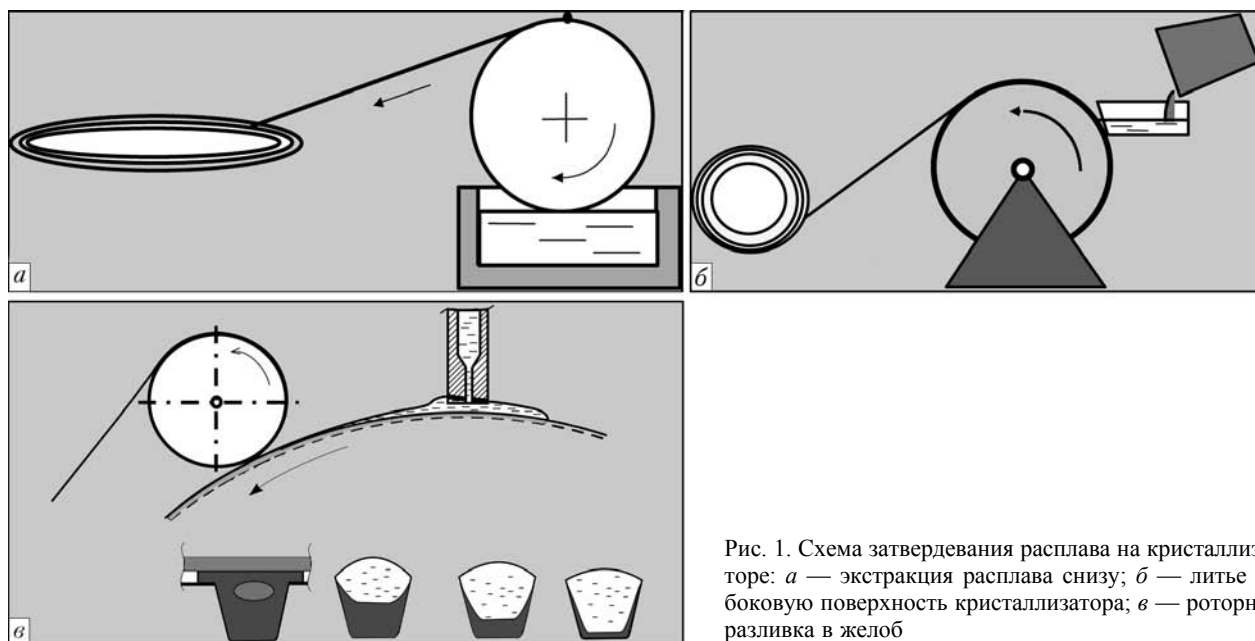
Схема затвердевания расплава на кристаллизаторе: *а* — экстракция расплава снизу; *б* — литье на боковую поверхность кристаллизатора; *в* — роторная разливка в желоб
